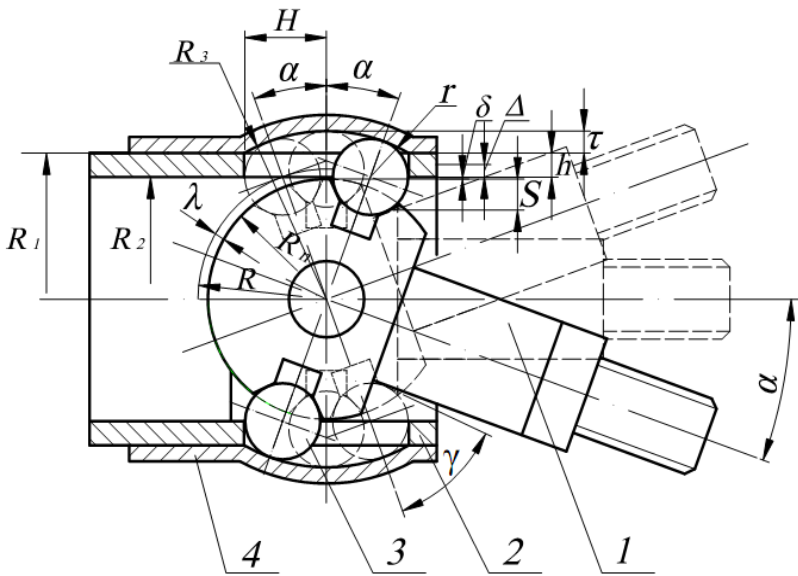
Розрахункова схема гнучкого шарнірного робочого органу
